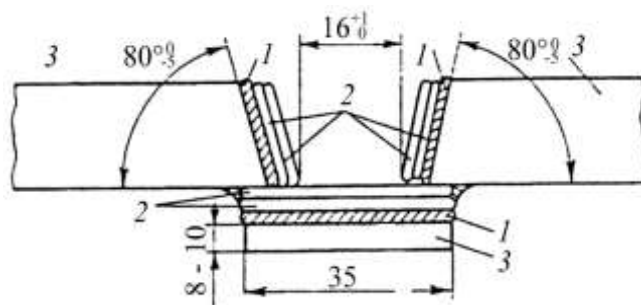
Схема підготовки кромки наплавленням для проби наплавленого металу:
